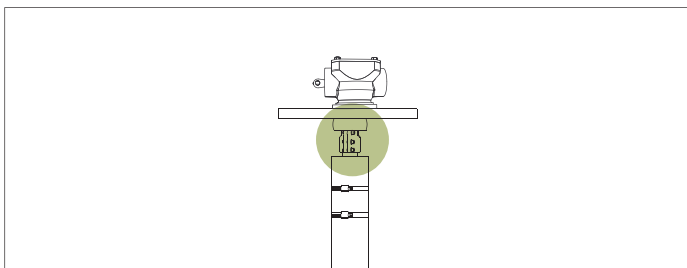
Присоединение вала квадратного сечения к коническому редуктору
